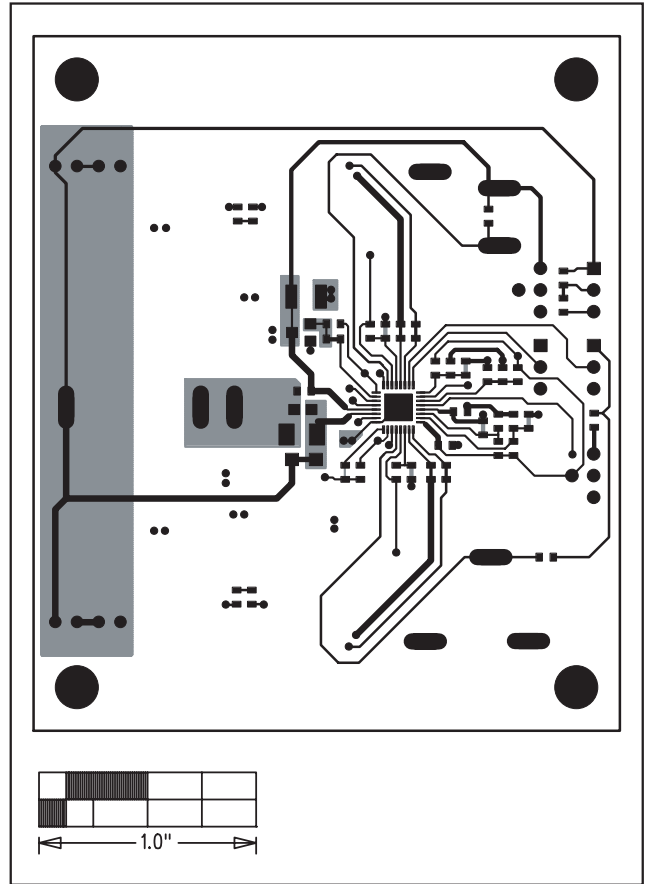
MAX1540 评估板 PCB 布局 – 焊接面
